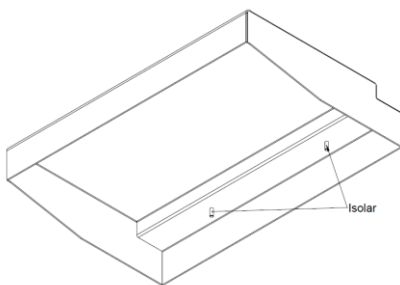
Representação 3D da Estrutura Soldada, pé 600mm
